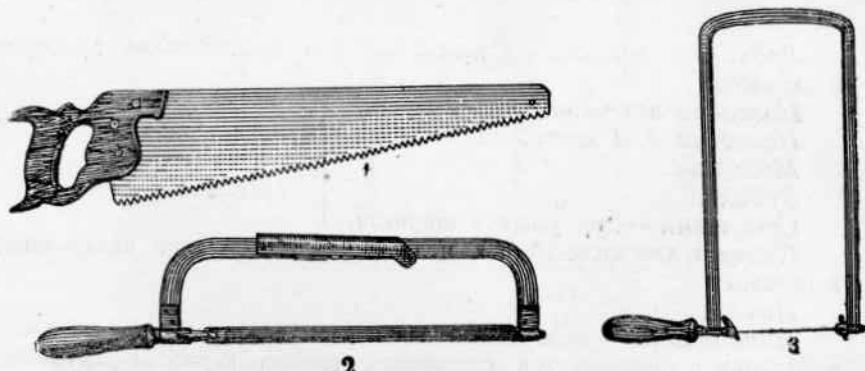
1 — ножовка для дерева; 2 — ножовка для металла;
